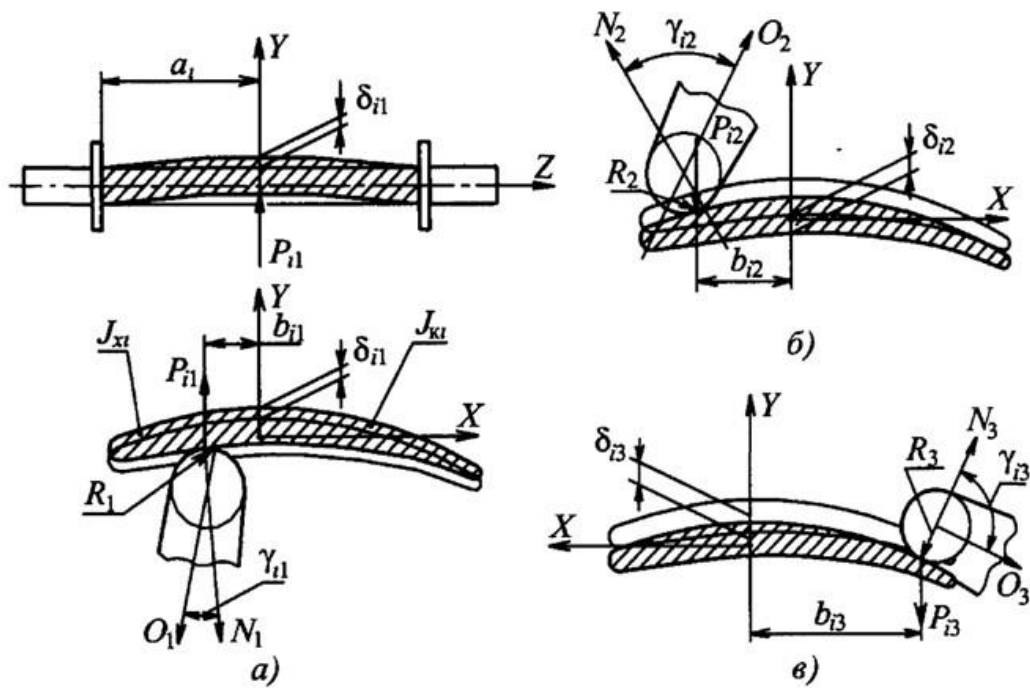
схеми до розрахунку деформації лопатки при круговому фрезеруванні.
